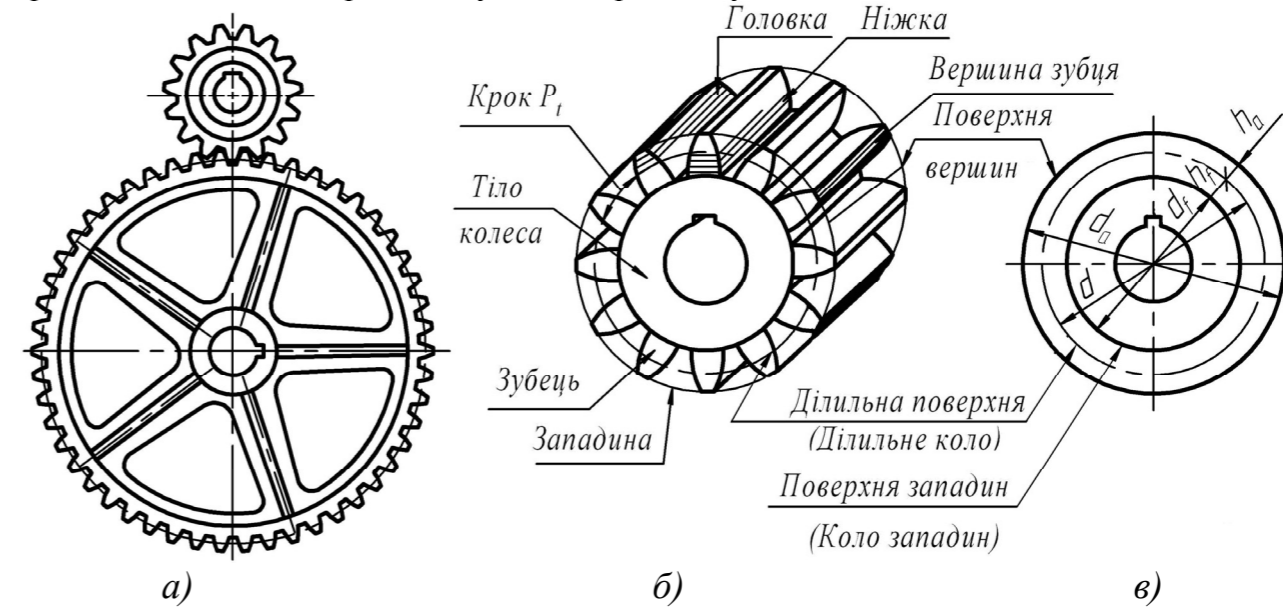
а – з'єднання циліндричних зубчастих коліс; б – позначення елементів зубчастого колеса; в – спрощене зображення зубчастого колеса
